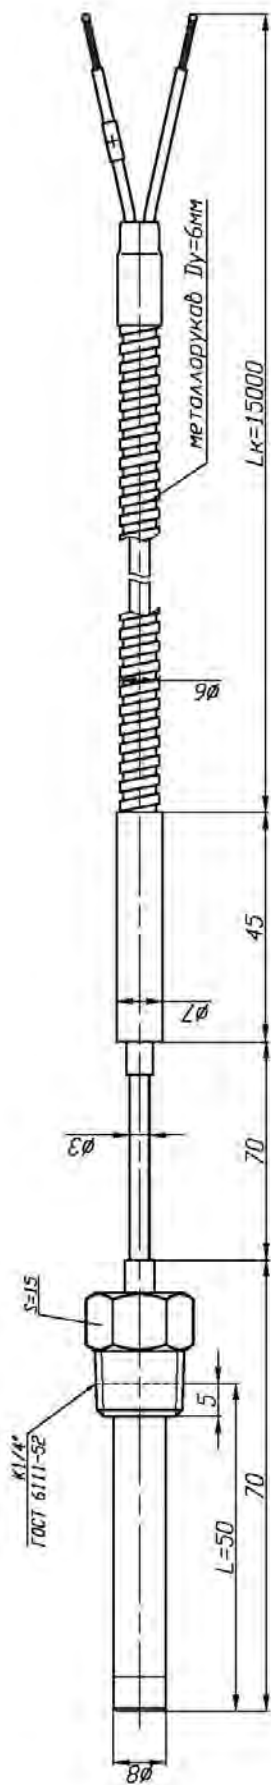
Габаритный чертеж ПТ исполнения ТХА 001Сп
